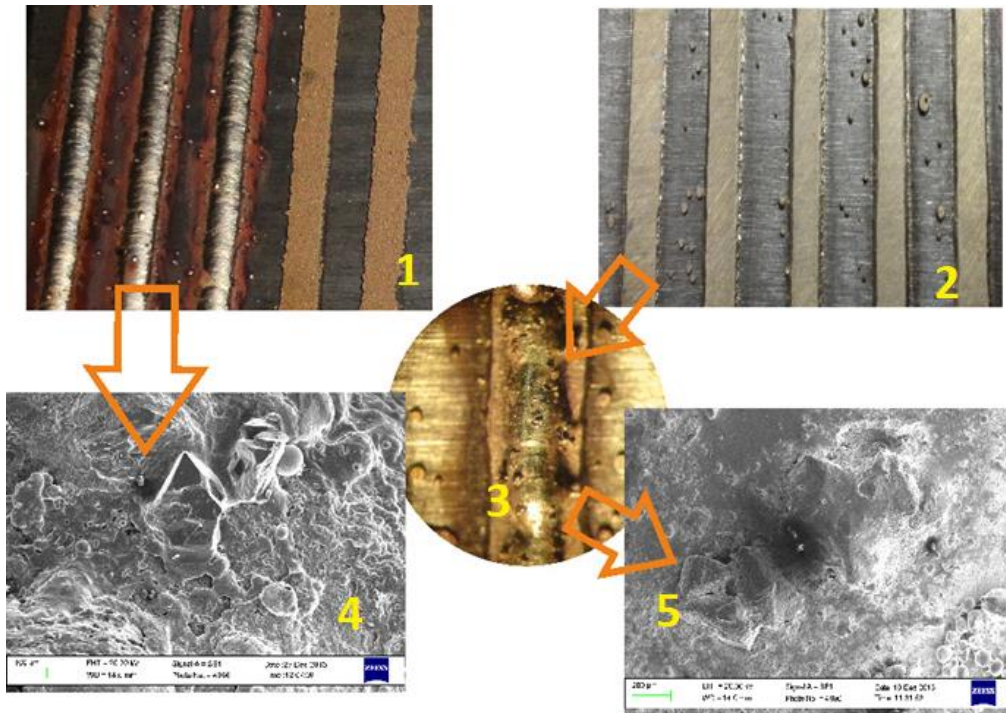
Процес формування на поверхні інструменту абразивного шару на плоскій поверхні:
